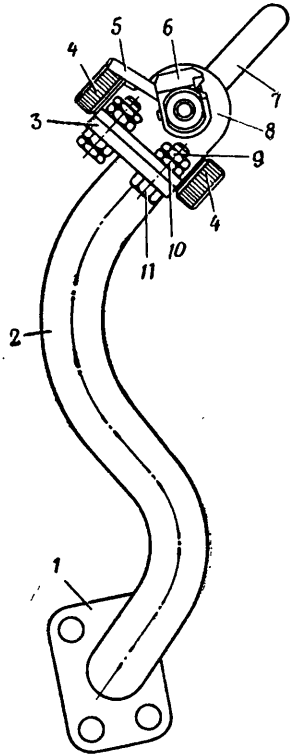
Приспособление для установки и крепления прицела (Сб17):
